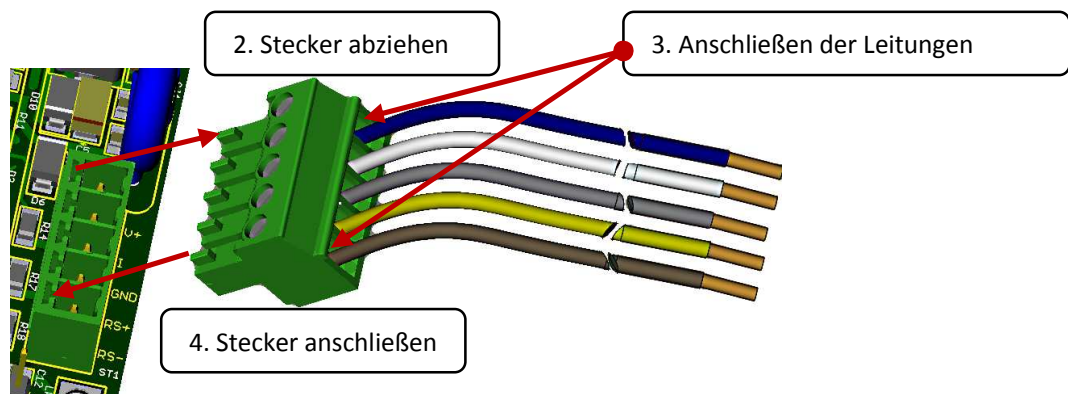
Der Kabelstecker MC 1,5-3,81, passend für das Grundgehäuse ST1 auf der Schnittstellenkarte
